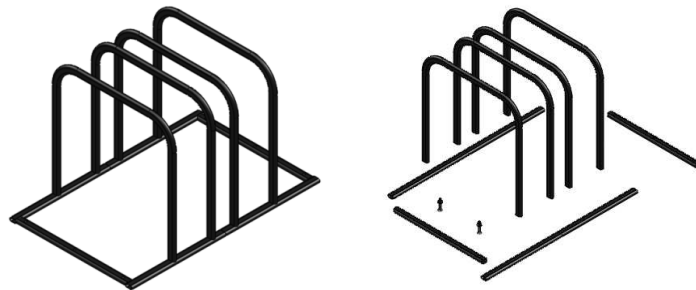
Conjunto base da cadeira, nas vistas isométrica e explodida.
